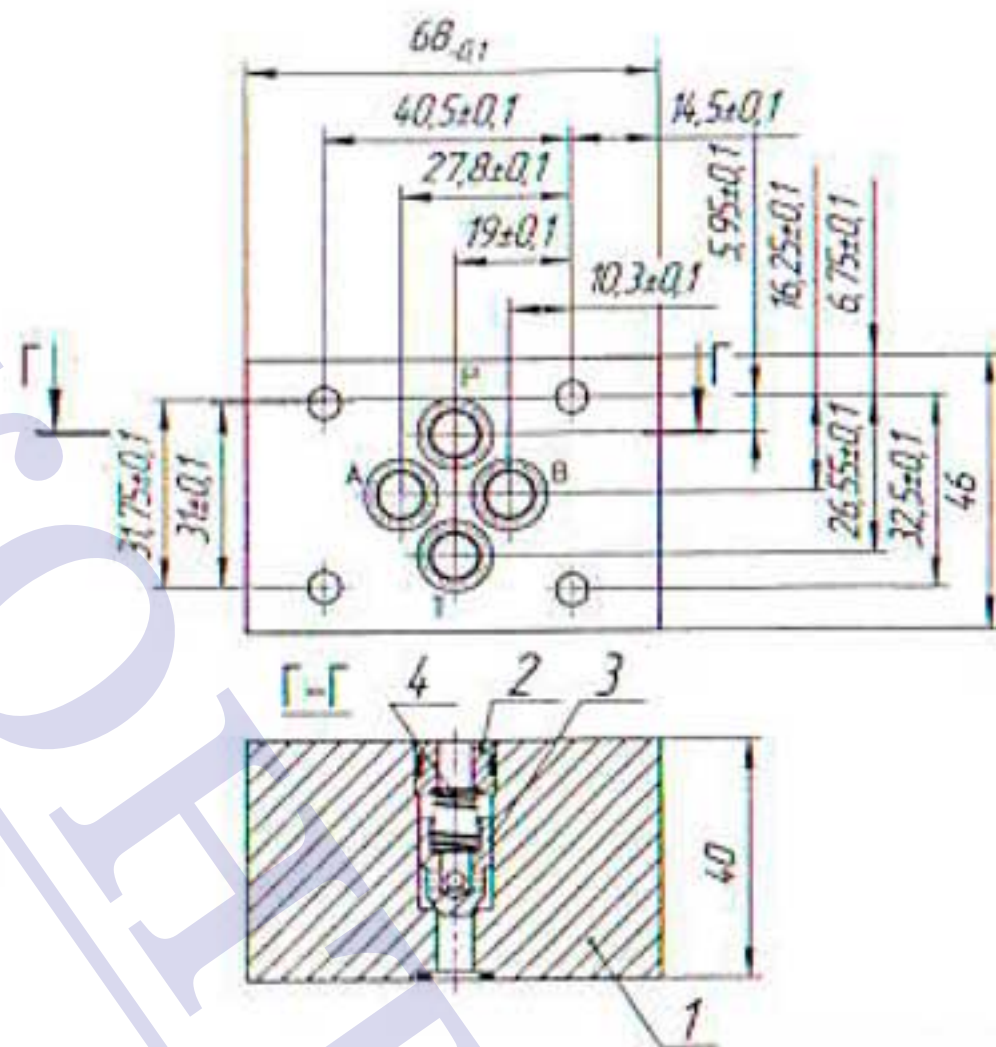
Основные габаритные и присоединительные размеры клапана обратного КОМ 6.3 Р-УХЛ1
